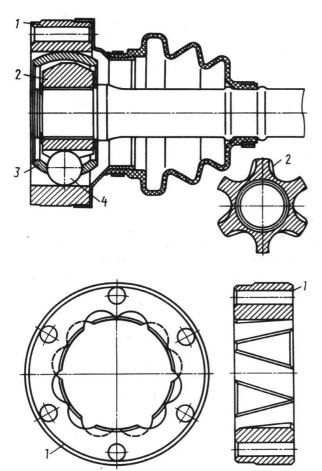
Шариковый универсальный шарнир (типа «Лебро»
